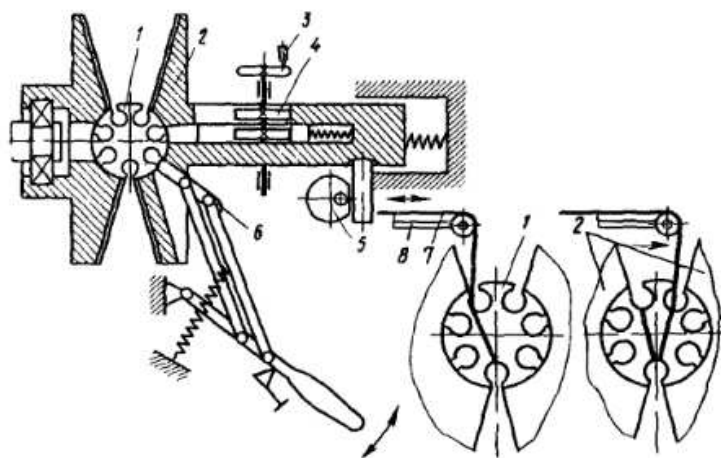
Намотка хордовой обмотки якоря на челночном станке
